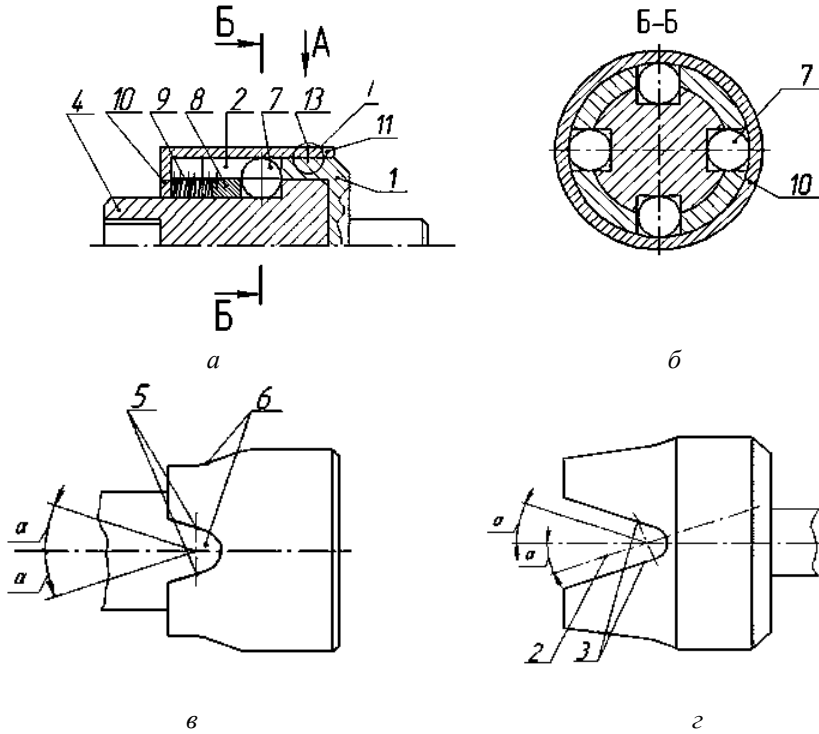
Принципова конструкція гайковерта: а – загальний вигляд; б – переріз Б-Б; в, г – вид А на ведену та ведучу півмуфти
